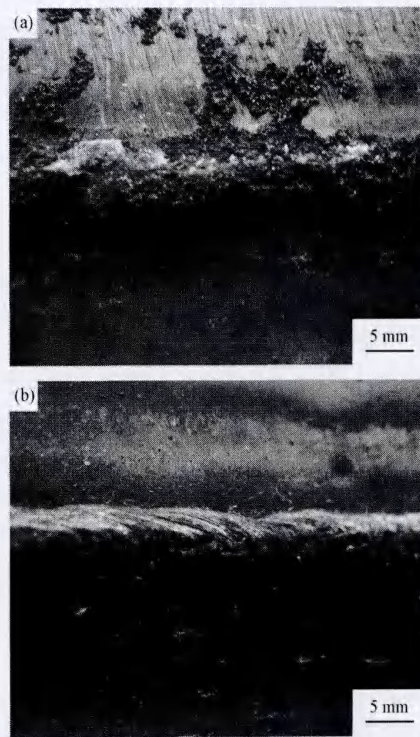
焊缝背面宏观照片 (a) 免充氩焊接; (b) 充氩焊接
